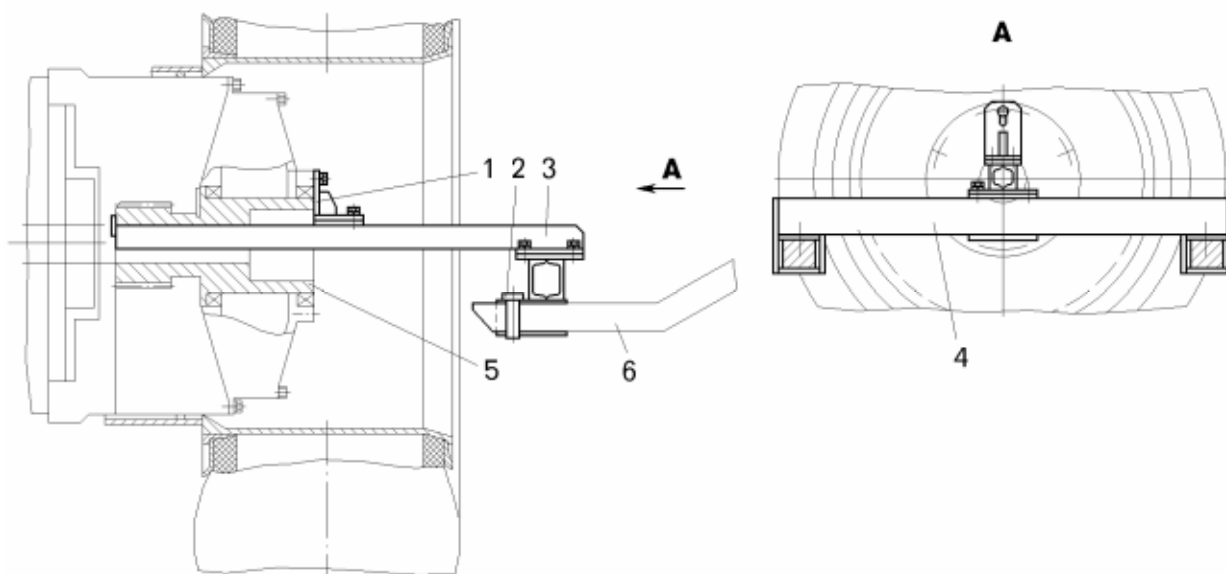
Приспособление для снятия и установки водила первого ряда:
